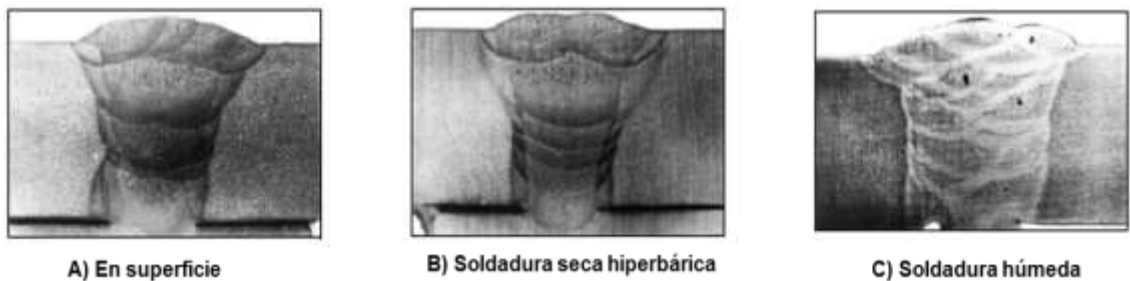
13 Macrografías de A) superficie, B) soldadura seca hiperbárica y C) soldadura húmeda (2).
